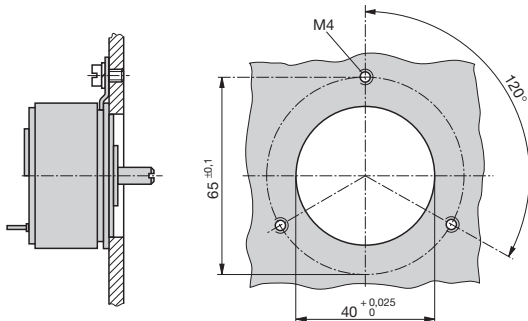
Bohrplan für Befestigung mit 3 Spannklemmen.
